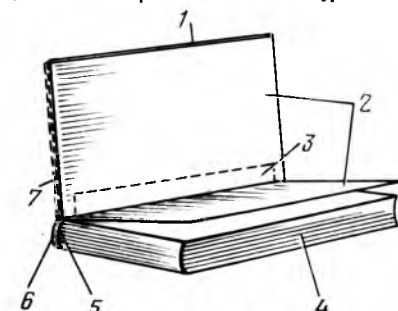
1 — крышка; 2 — форзац; 3 — марля; 4 — блок журналов; 5 — каптал; 6 — корешок; 7 — картонная сторона
